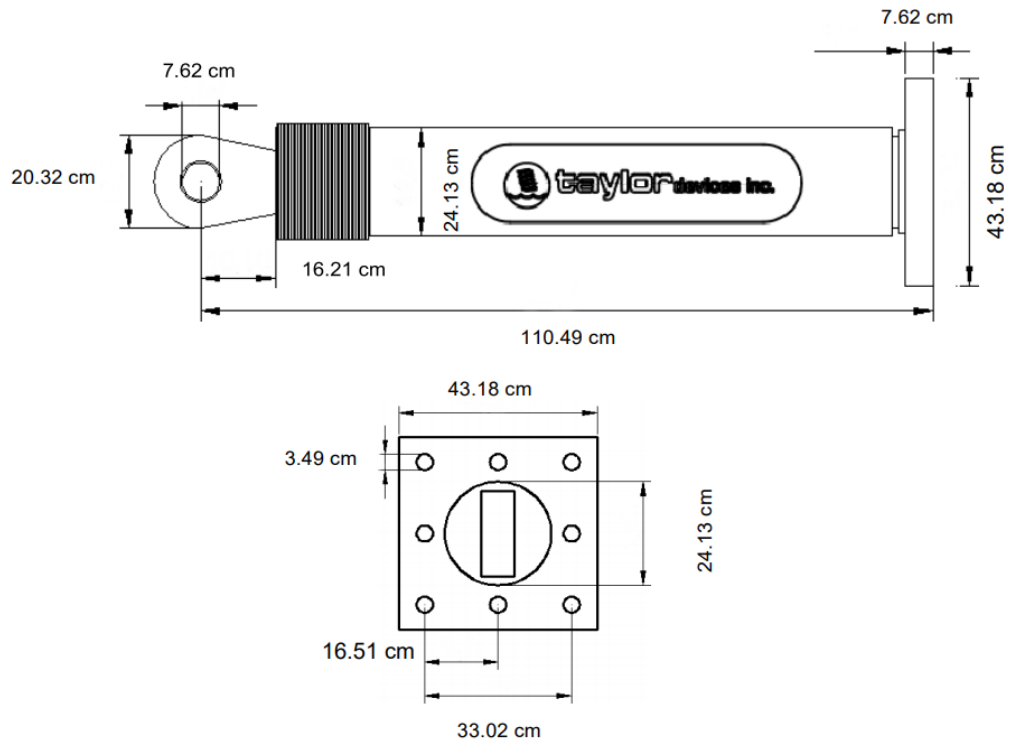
Dimensiones de disipador y placa base de 330 Kip.
